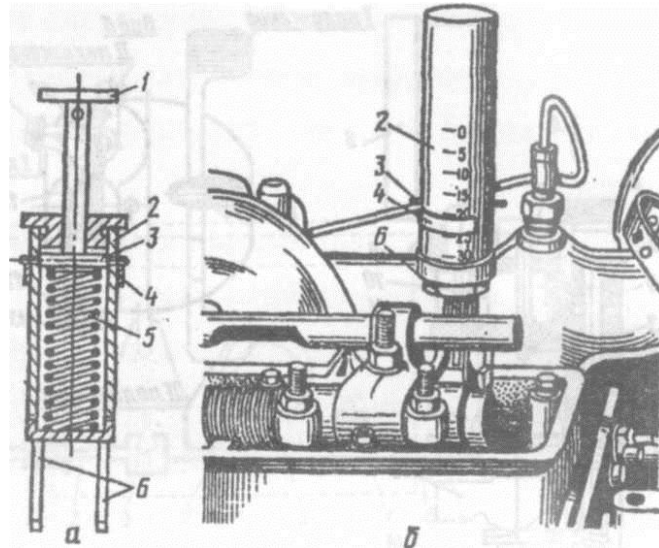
Перевірка пружності пружини клапанів газорозподілу приладом КИ-723: а - прилад для перевірки зусилля притискування клапанів до сідел головки циліндрів; б - визначення зусилля притискування клапану до сидла; 1 - рукоятка приладу; 2 - корпус; 3 - натискний штифт; 4 - кільце-фіксатор; 5 - пружина; 6 - встановлювальні стійки.
